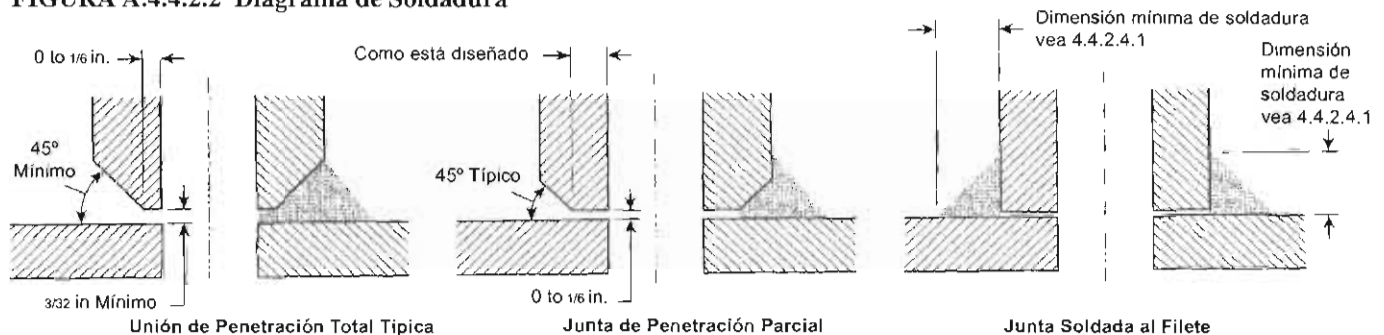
Descripciones de Soldadura
